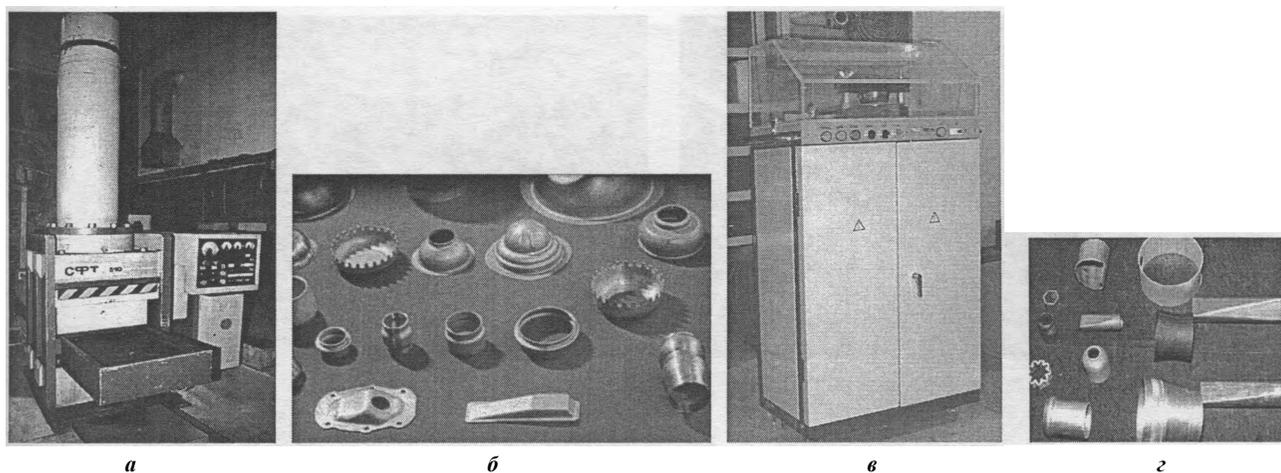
Прессы импульсной листовой штамповки (а) и магнитно-импульсной штамповки (в), образцы деталей (б, г)
